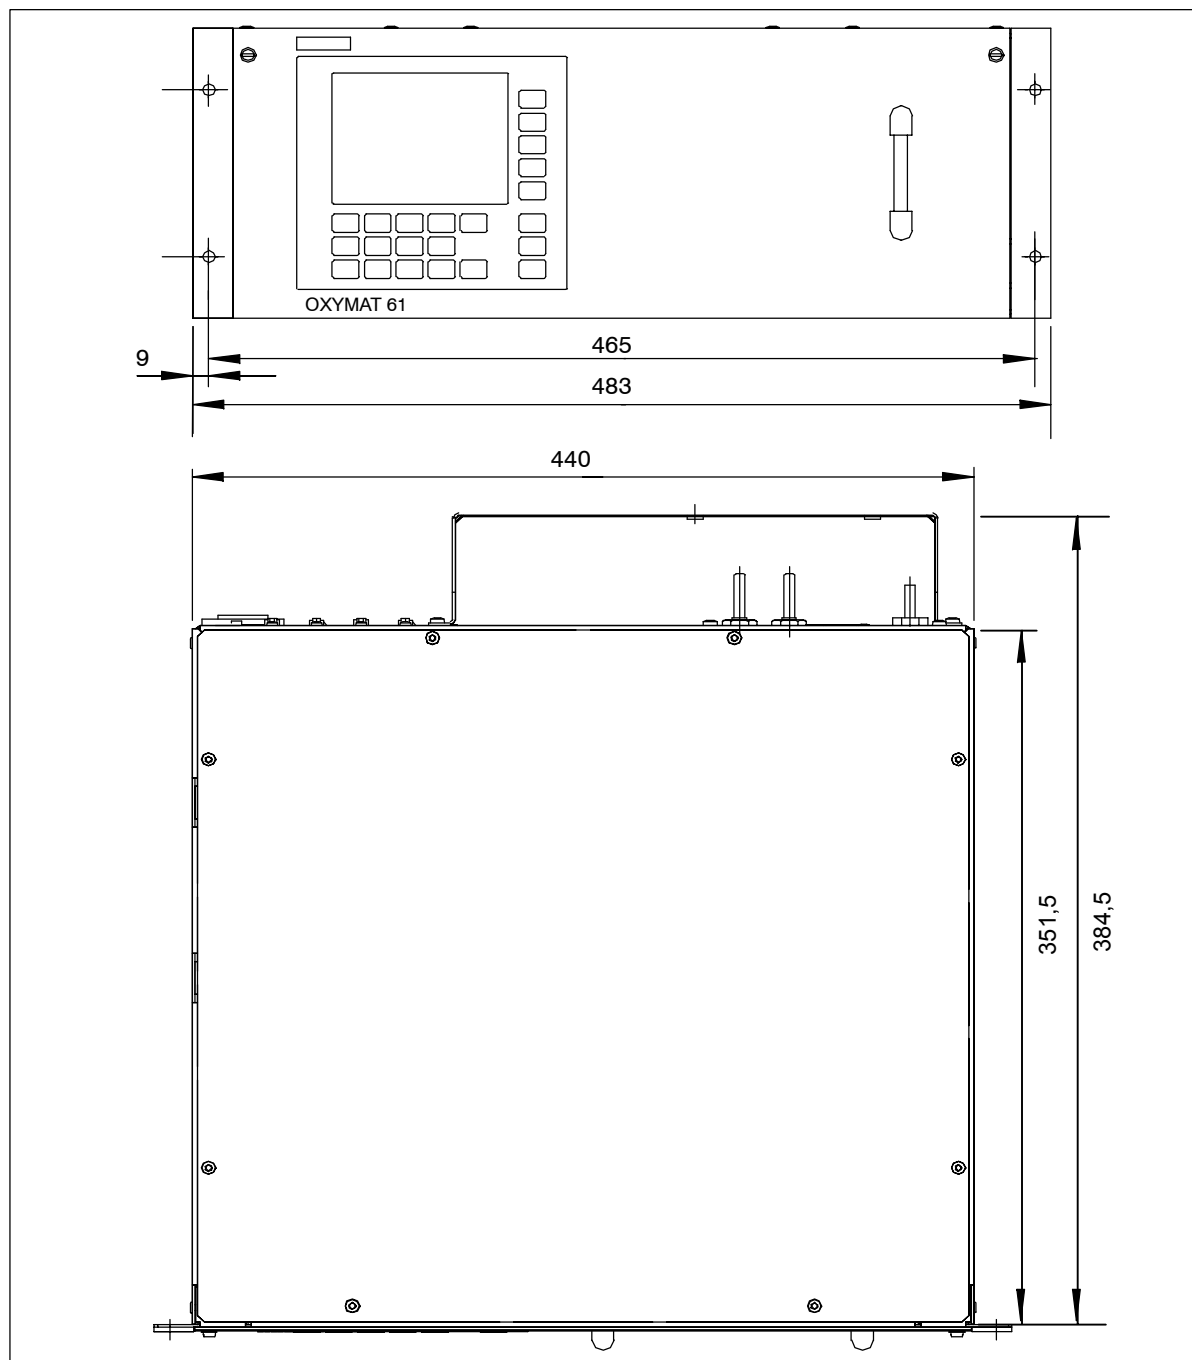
Dimensioni per la preparazione del montaggio (visto frontale e dall'alto)
